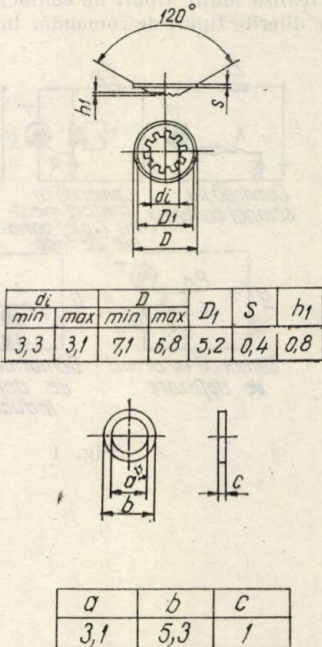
Sistem de montaj pe radiator al capsulei SOT-32 și accesoriile specifice (dimensiuni în mm):
